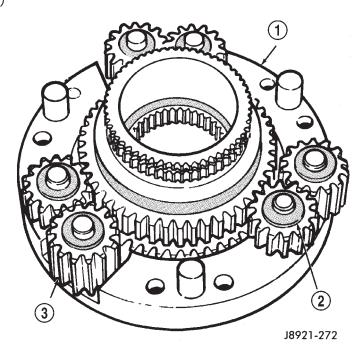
Desmontaje de engranajes planetarios y arandelas de empuje
